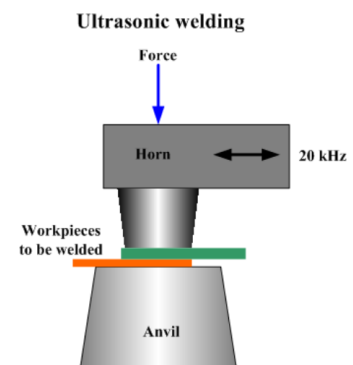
Soldadura ultrasónica. Fuente: Substech.
